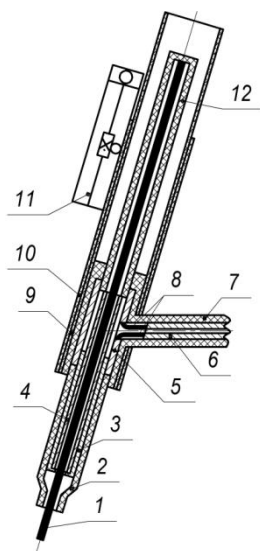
Конструкция устройства горелки для реализации системы автоматической стабилизации ручной и механизированной аргодуговой сварки
